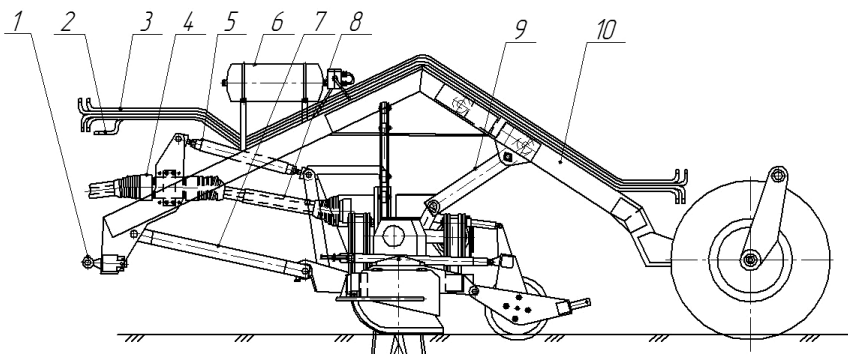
Схема почвообрабатывающего адаптера (вид сбоку):
